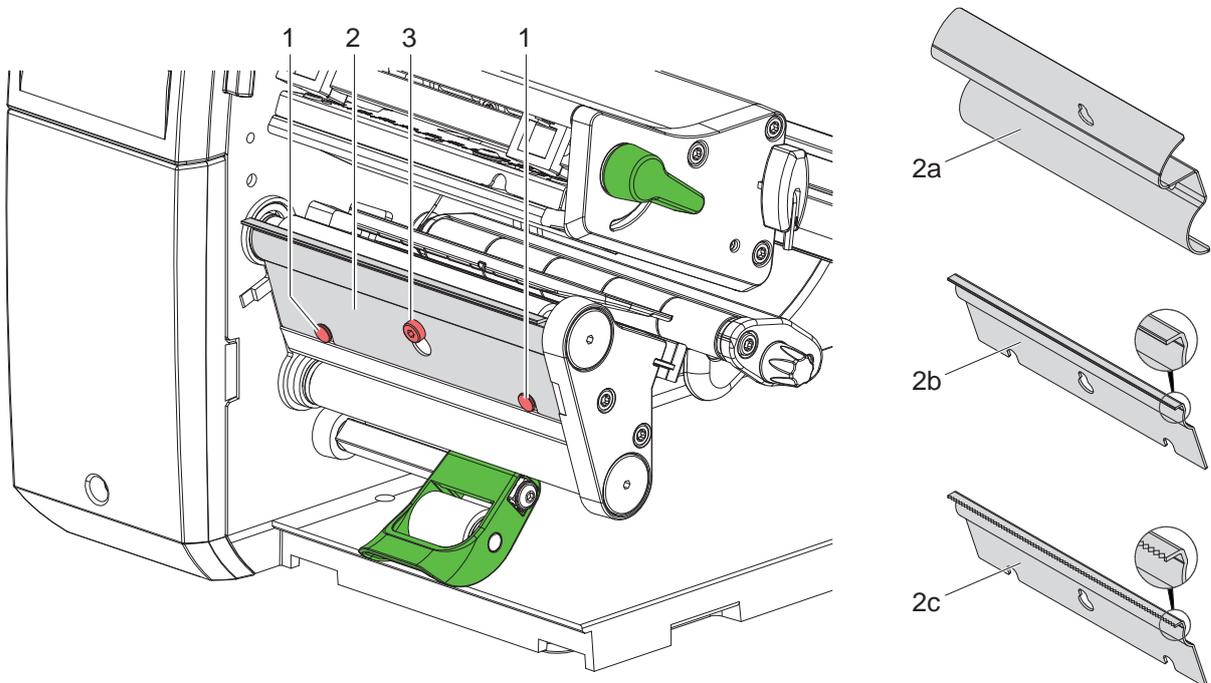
Монтаж и демонтаж перегородки, датчика запроса или отрывной кромки
